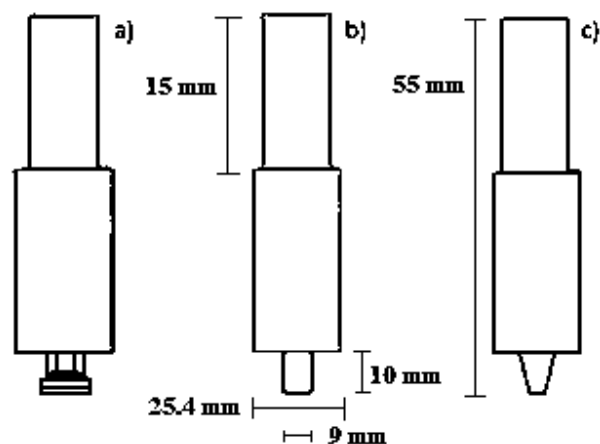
Herramientales utilizados para el proceso de soldadura por fricción-agitación. a) Pin cabeza de clavo, b) Pin cilíndrico y c) Pin cónico.
